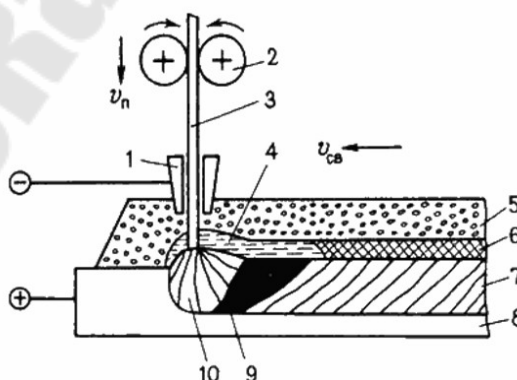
Схема механизированной наплавки металла под слоем флюса: 1 – токоподводящие колодки; 2 – подающие ролики; 3 – электродная проволока; 4 – слой шлака; 5 – слой сухого флюса; 6 – шлаковая корка; 7 – сварной шов (наплавленный металл); 8 – основной металл; 9 – сварочная ванна; 10 – электрическая дуга
